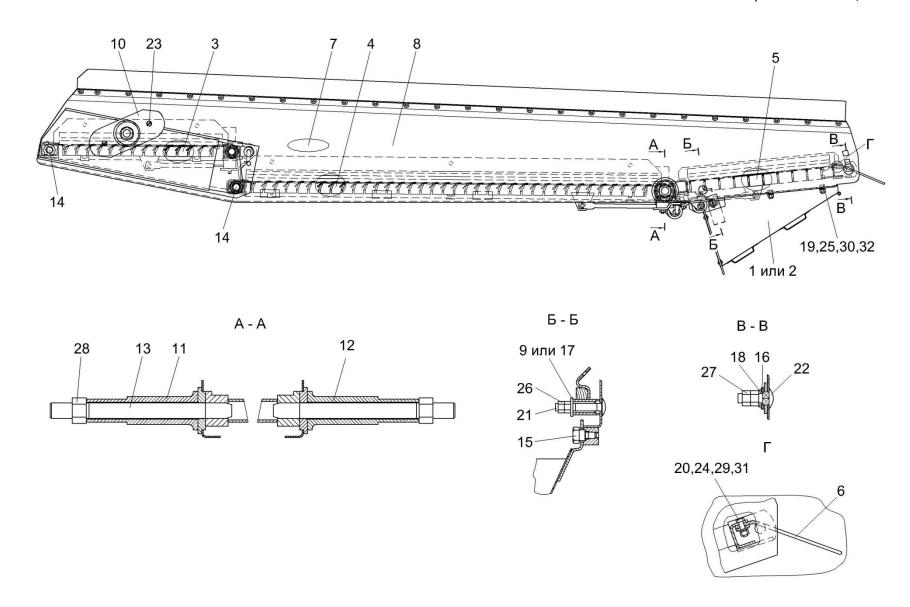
Стан решетный верхний КЗК 0260000Б-01
